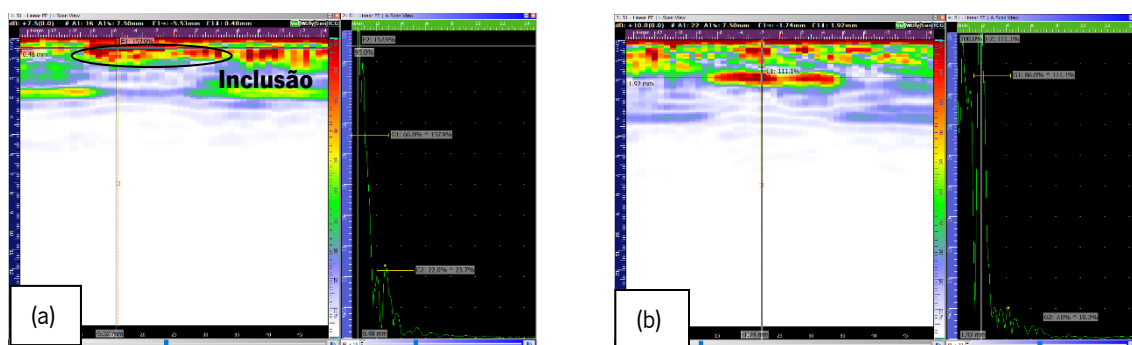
(a) Inclusão de fita adesiva de dimensões 8×8 mm² colocada na zona de espessura 3,13 mm; (b) inclusão de fita adesiva de dimensões 10×10 mm² colocada na zona de espessura 4,04 mm.
